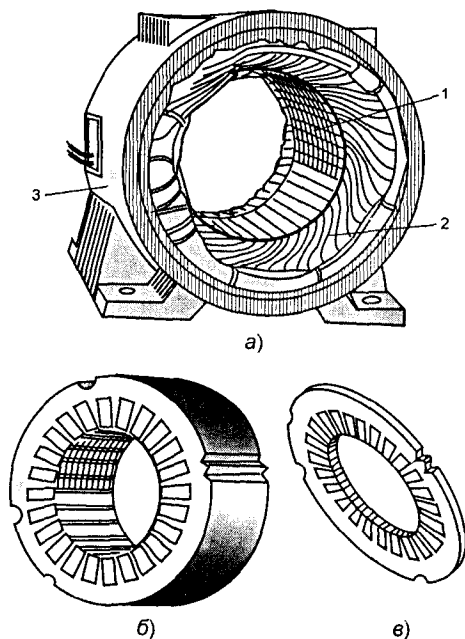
Статор асинхронного электродвигателя: *а* — статор в сборе; *б* — сердечник статора; *в* — лист сердечника; 1 — сердечник; 2 — обмотка; 3 — корпус (станина)
